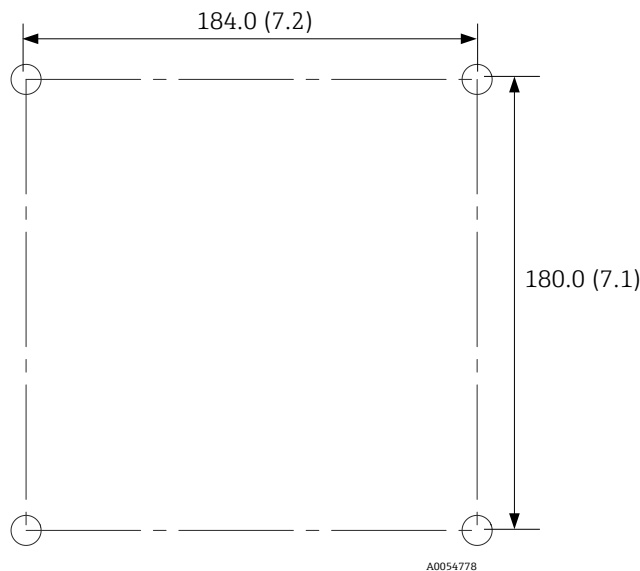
Schema dei fori di montaggio della custodia MAC. Dimensioni: mm (in)
